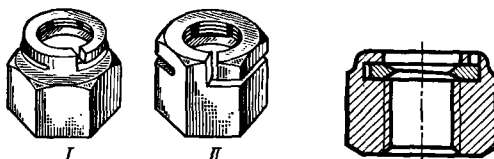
Гайки с самозатягивающимся витком: I — корончатая; II — шестигранная
